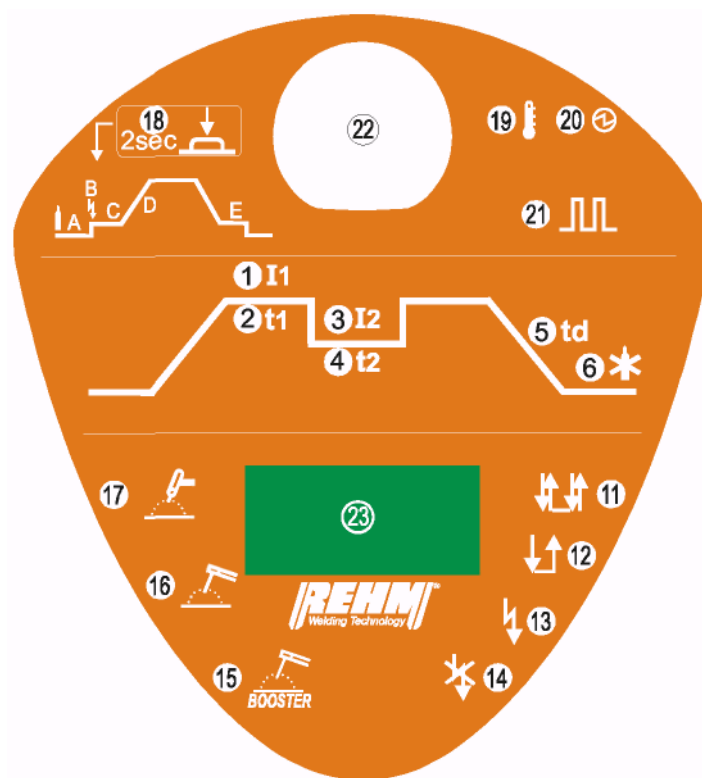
Панель управления сварочных аппаратов TIGER 170 DC и Tiger 210 DC.
